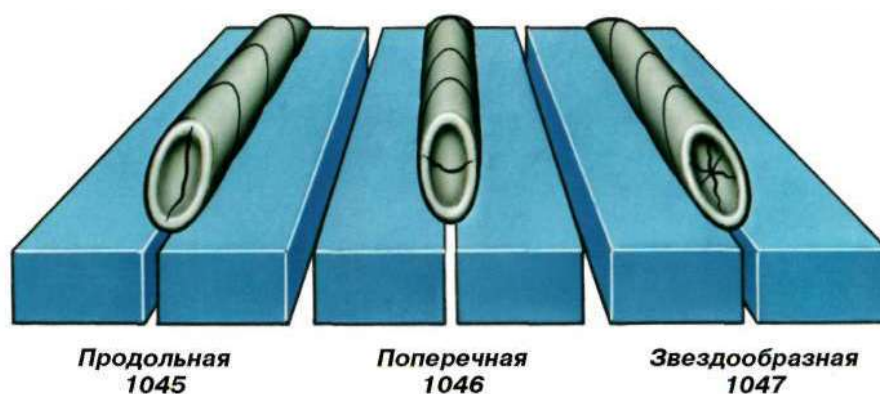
Дефекты сварного шва по типу трещин в кратере
